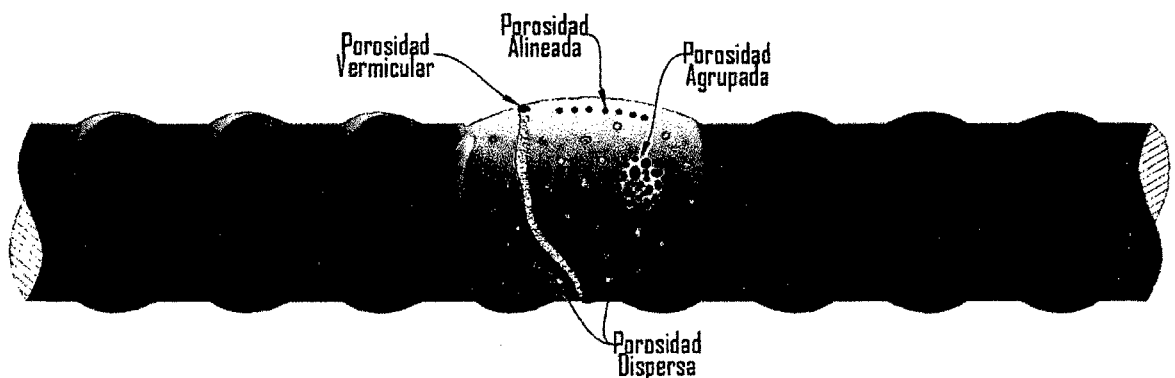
Tipos de Porosidad en la soldadura
